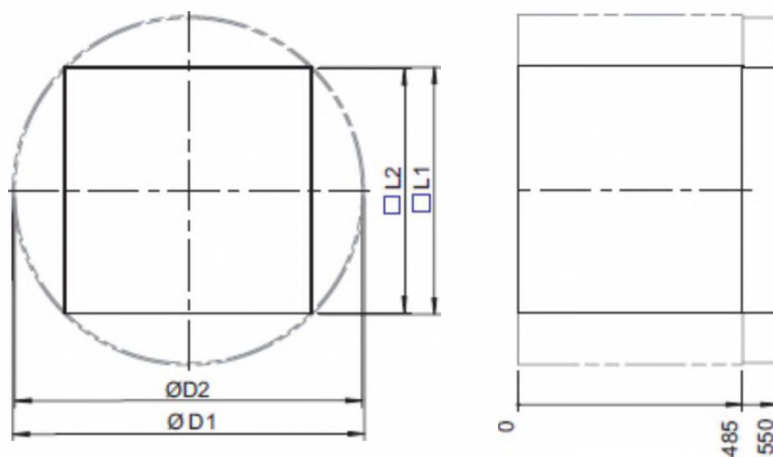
Габаритні розміри деталі при положенні столу 0°
